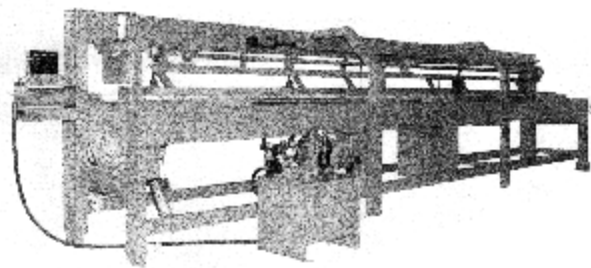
Общий вид прессы для сращивания заготовок марки ПССТ-6,75-20 фирмы Горлуш (Киев)
